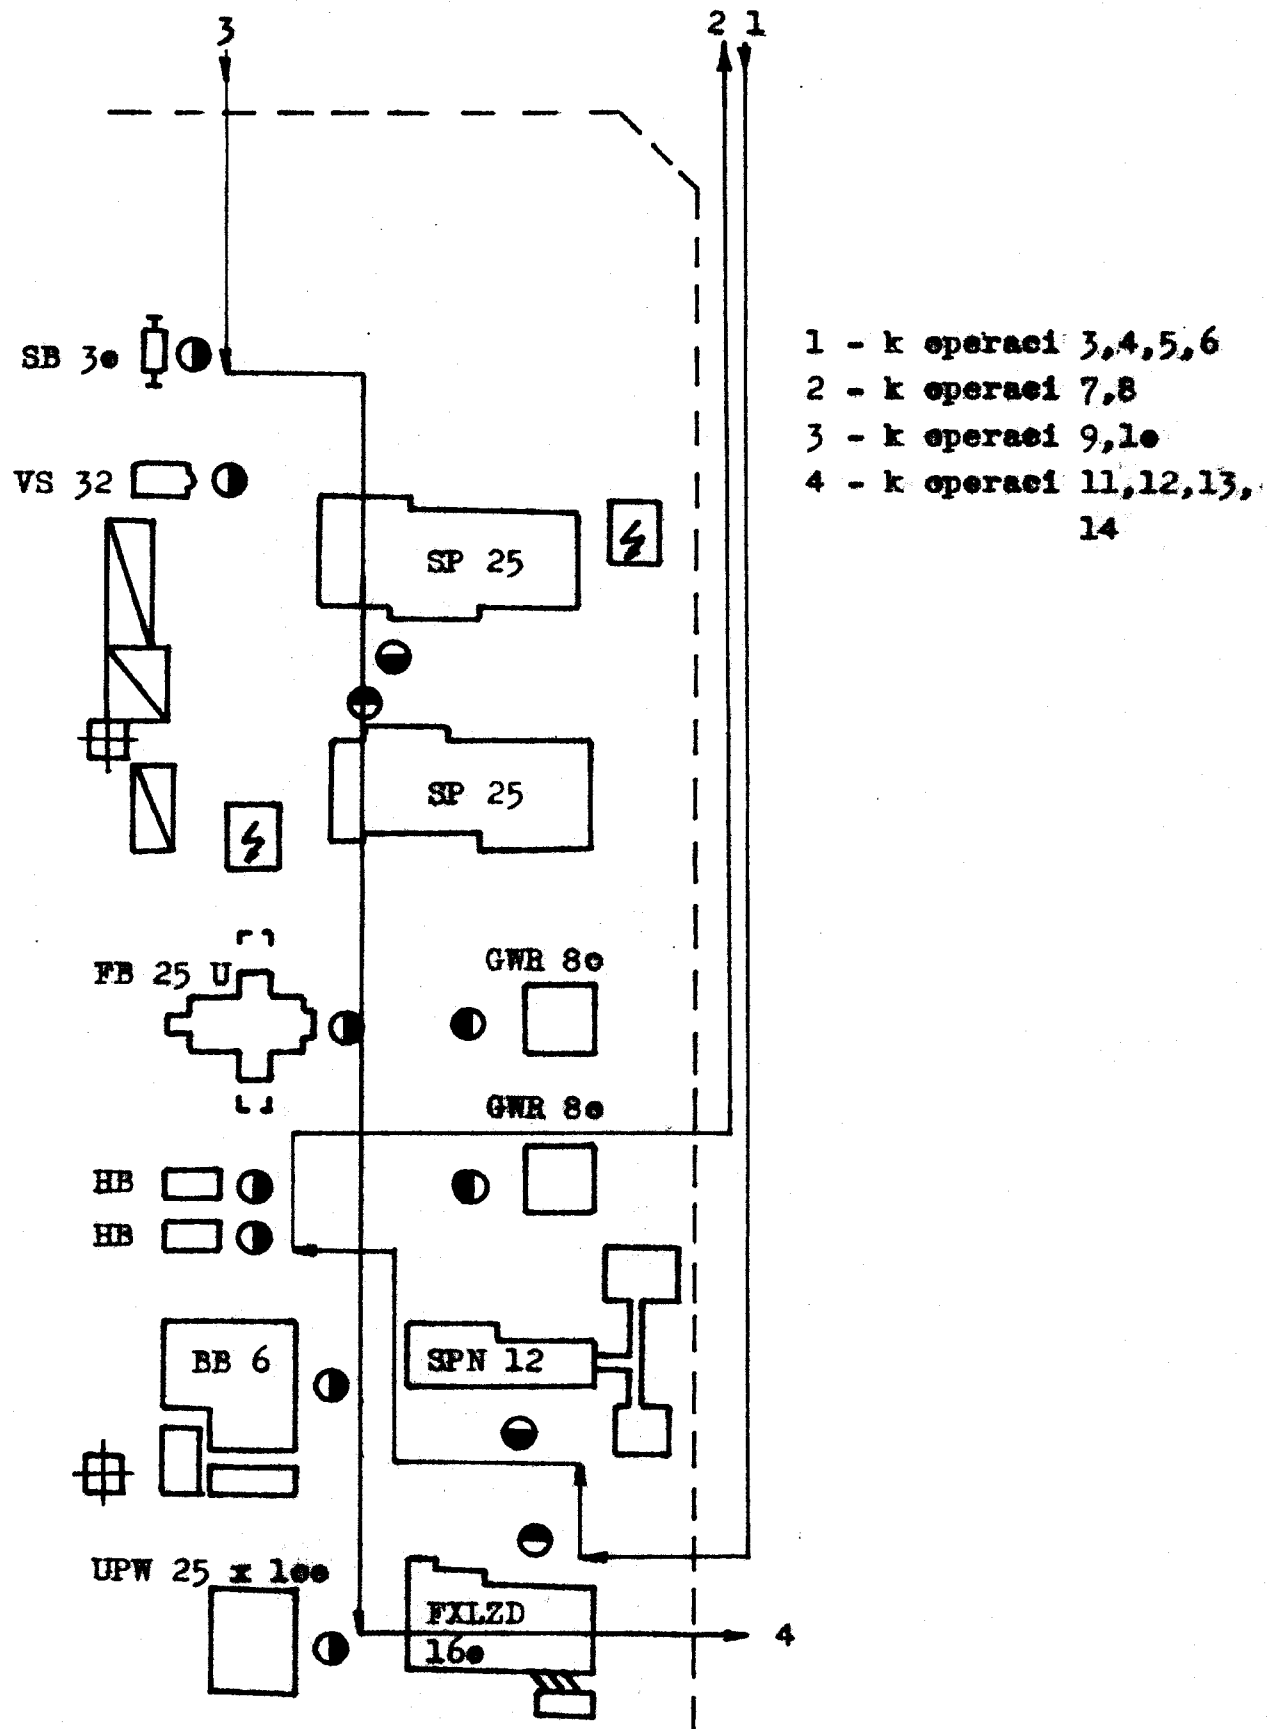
Materiálový tok při výrobě šroubu ojniční hlavy
